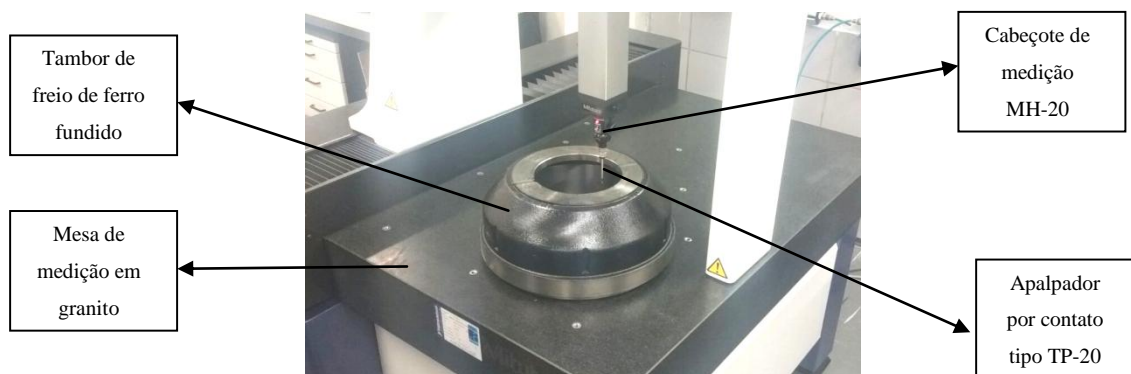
Tambor de freio montado sobre a mesa de medição da MMC
